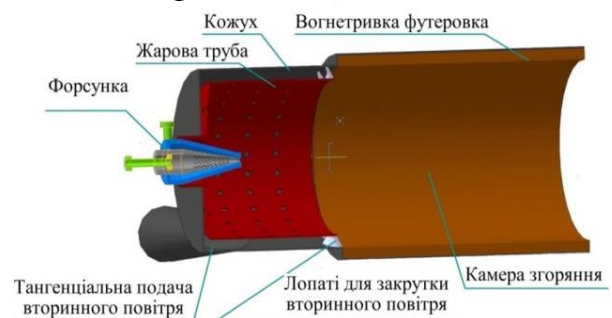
Схема пального пристрою для спалювання композиційного палива
